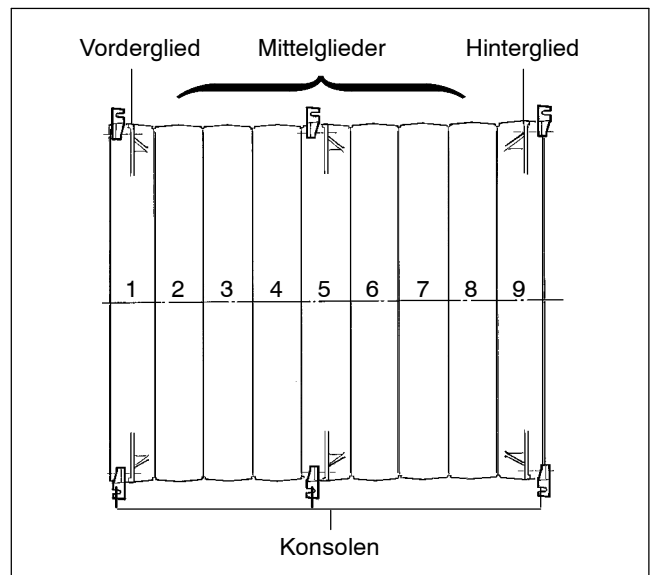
Draufsicht; Kesselblock 9 Gld. mit Konsolen
